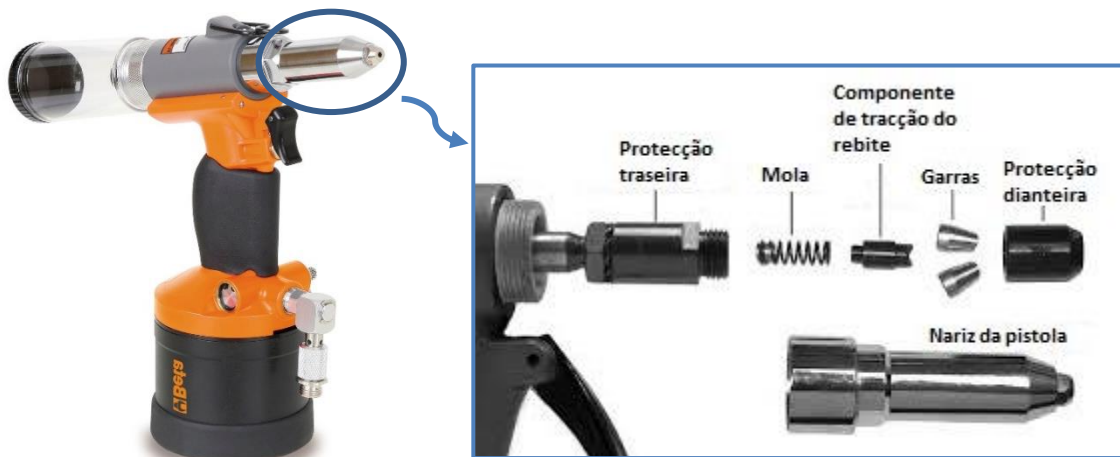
Constituintes gerais da pistola de rebitagem [Adaptado de (Beta-Werkzeuge.de) e (JET, 2015)].
